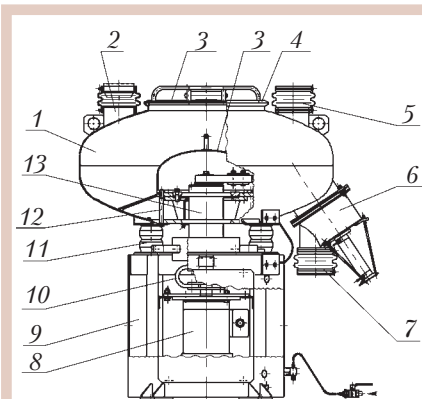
Смеситель вибрационный СМВ-0,4: 1 – камера; 2 – патрубок загрузки; 3 – крышки; 4 – хомут; 5 – герметизатор; 6 – клапан; 7 – патрубок разгрузки; 8 – двигатель; 9 – рама; 10 – муфта; 11 – виброизолятор; 12 – болт; 13 – вибровозбудитель
